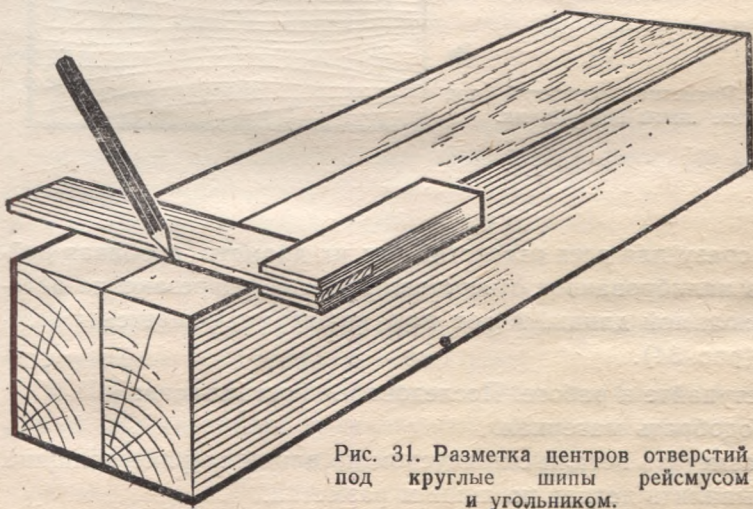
Разметка центров отверстий под круглые шипы рейсмусом и угольником.
